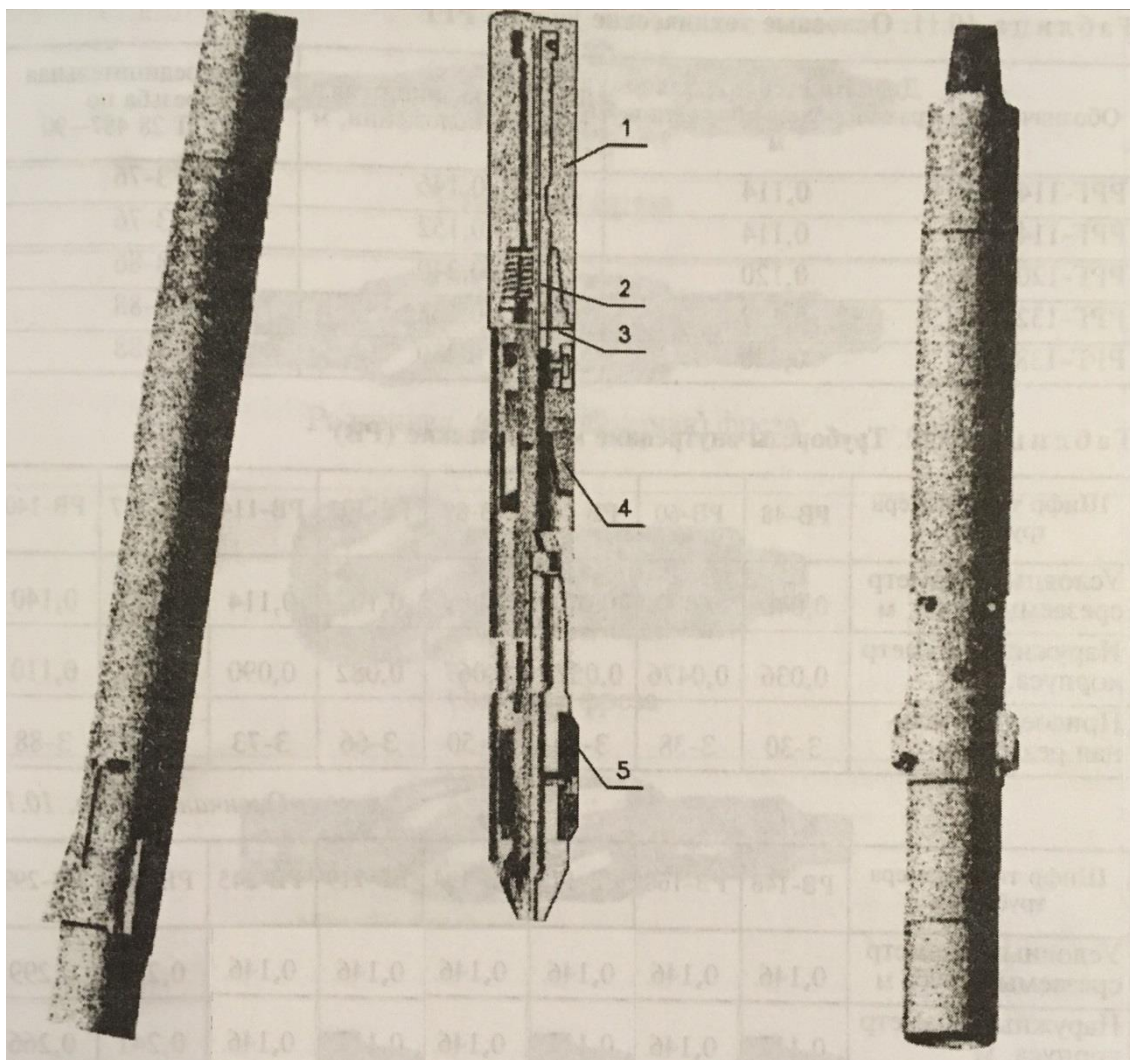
Внешний вид фрезера типа ФР; Расширитель типа РР;
